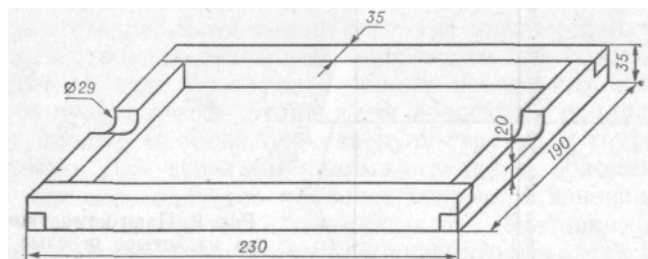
Рама-подставка для разборки и сборки винтовок ИЖ-38 (ИЖ-22)
